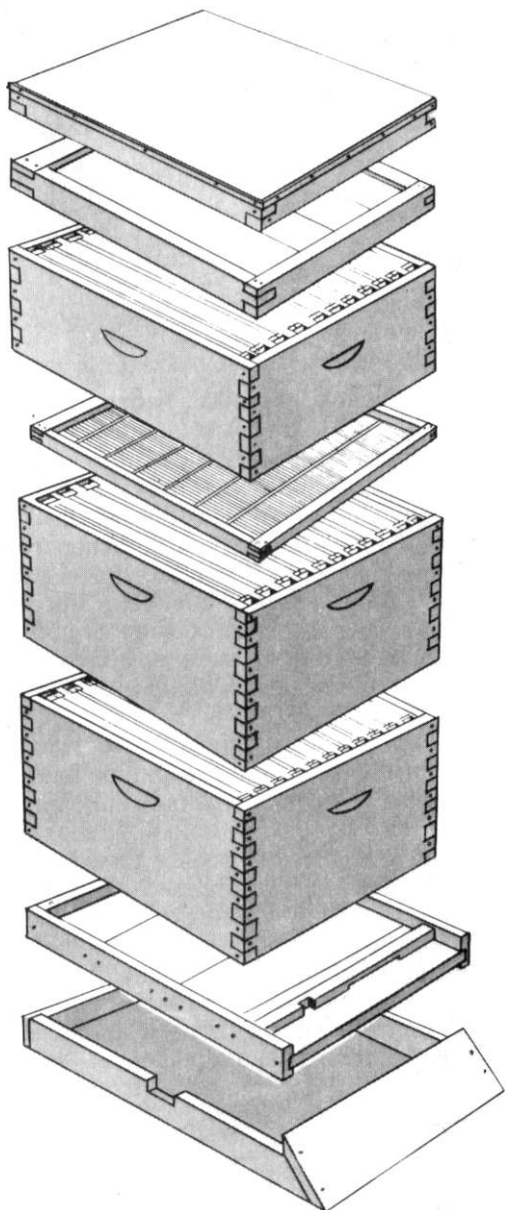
Многокорпусный улей (сверху вниз: крыша, потолок, магазин, разделительная решетка, два корпуса, пол с вкладышем, подставка).
